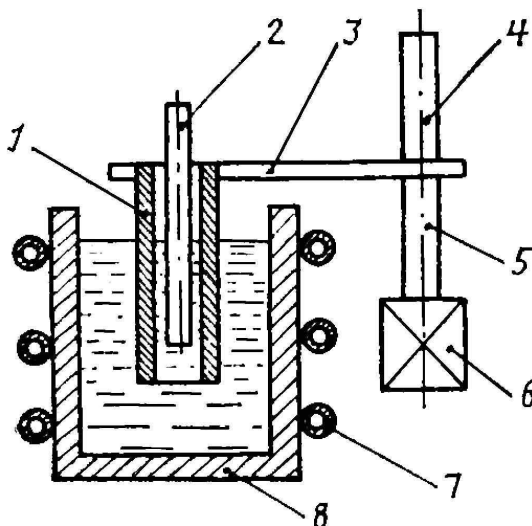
Устройство для ультразвукового лужения длинномерных изделий: 1 – трубчатый излучатель ультразвука; 2 – обрабатываемое изделие; 3 – пластинчатый волновод; 4, 5 – волноводы; 6 – ультразвуковой преобразователь; 7 – нагреватель; 8 – ванна
